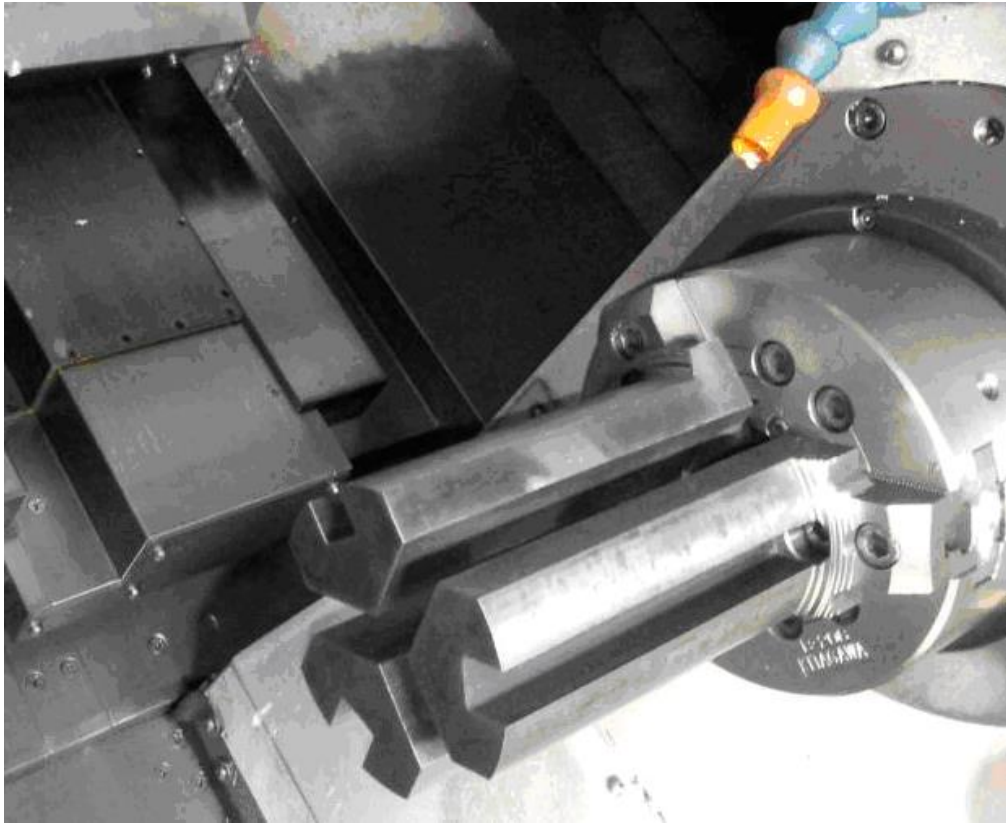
Трехкулачковый самоцентрирующий патрон с удлиненными широкими кулачками для обработки наружной поверхности
